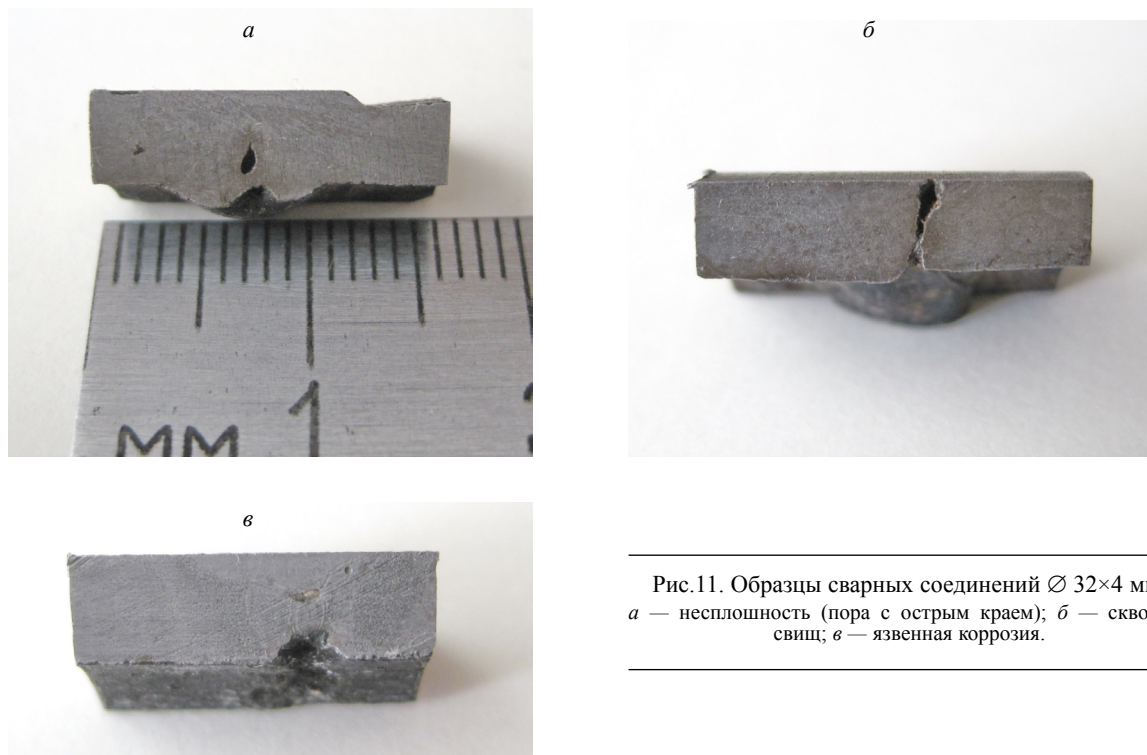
Образцы сварных соединений $\varnothing 32 \times 4$ мм:
